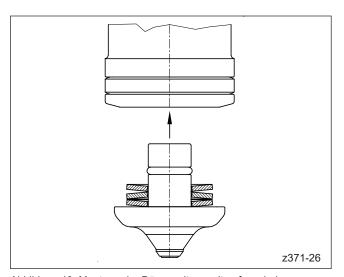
Montage der Düsenspitzen mit aufgeschobenen Tellerfedern (im Bild Beispiel mit 3 Tellerfedern) und O-Ring
